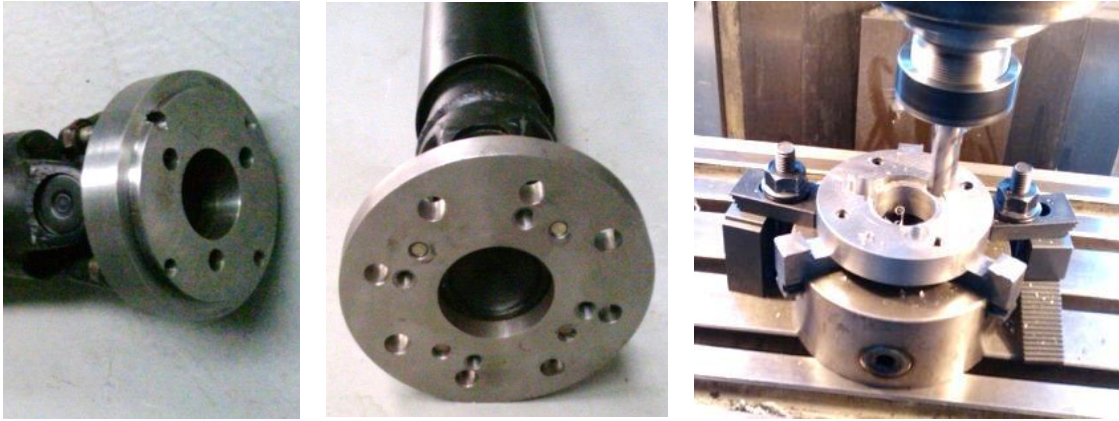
À esquerda a flange da cambota; ao centro a flange do freio; à direita a maquinagem de uma flange
